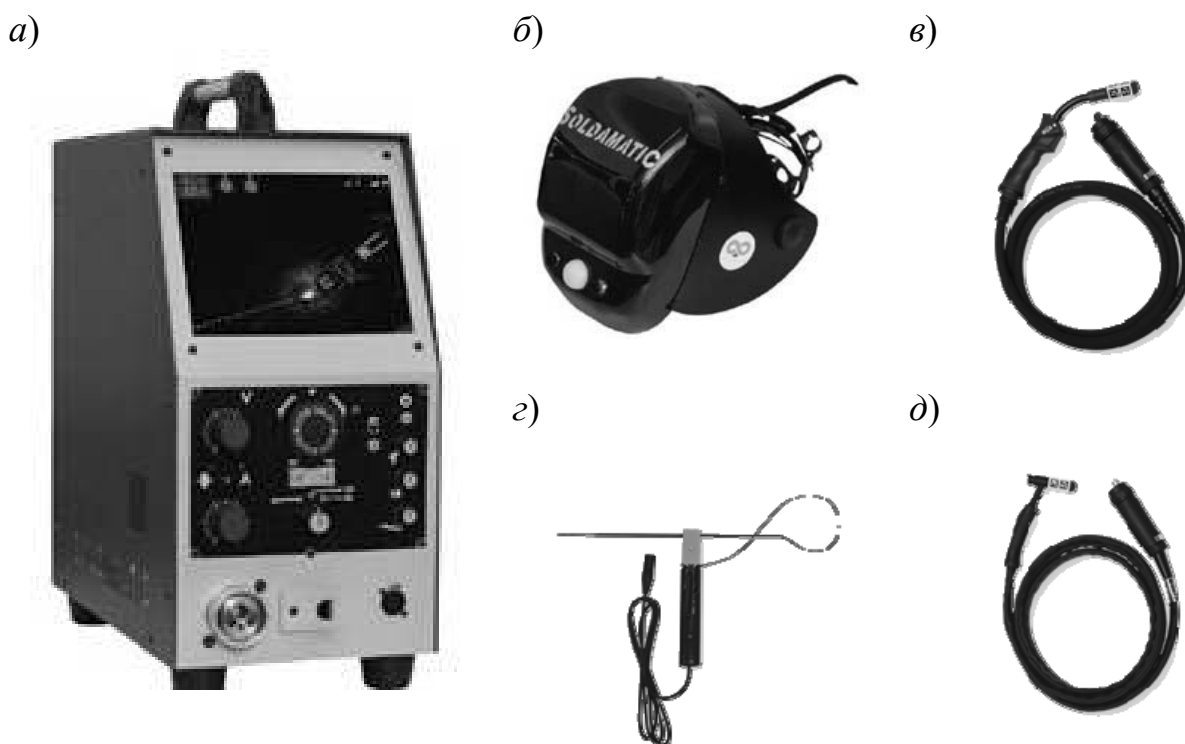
Оборудование, входящее в состав установки Soldamatic
